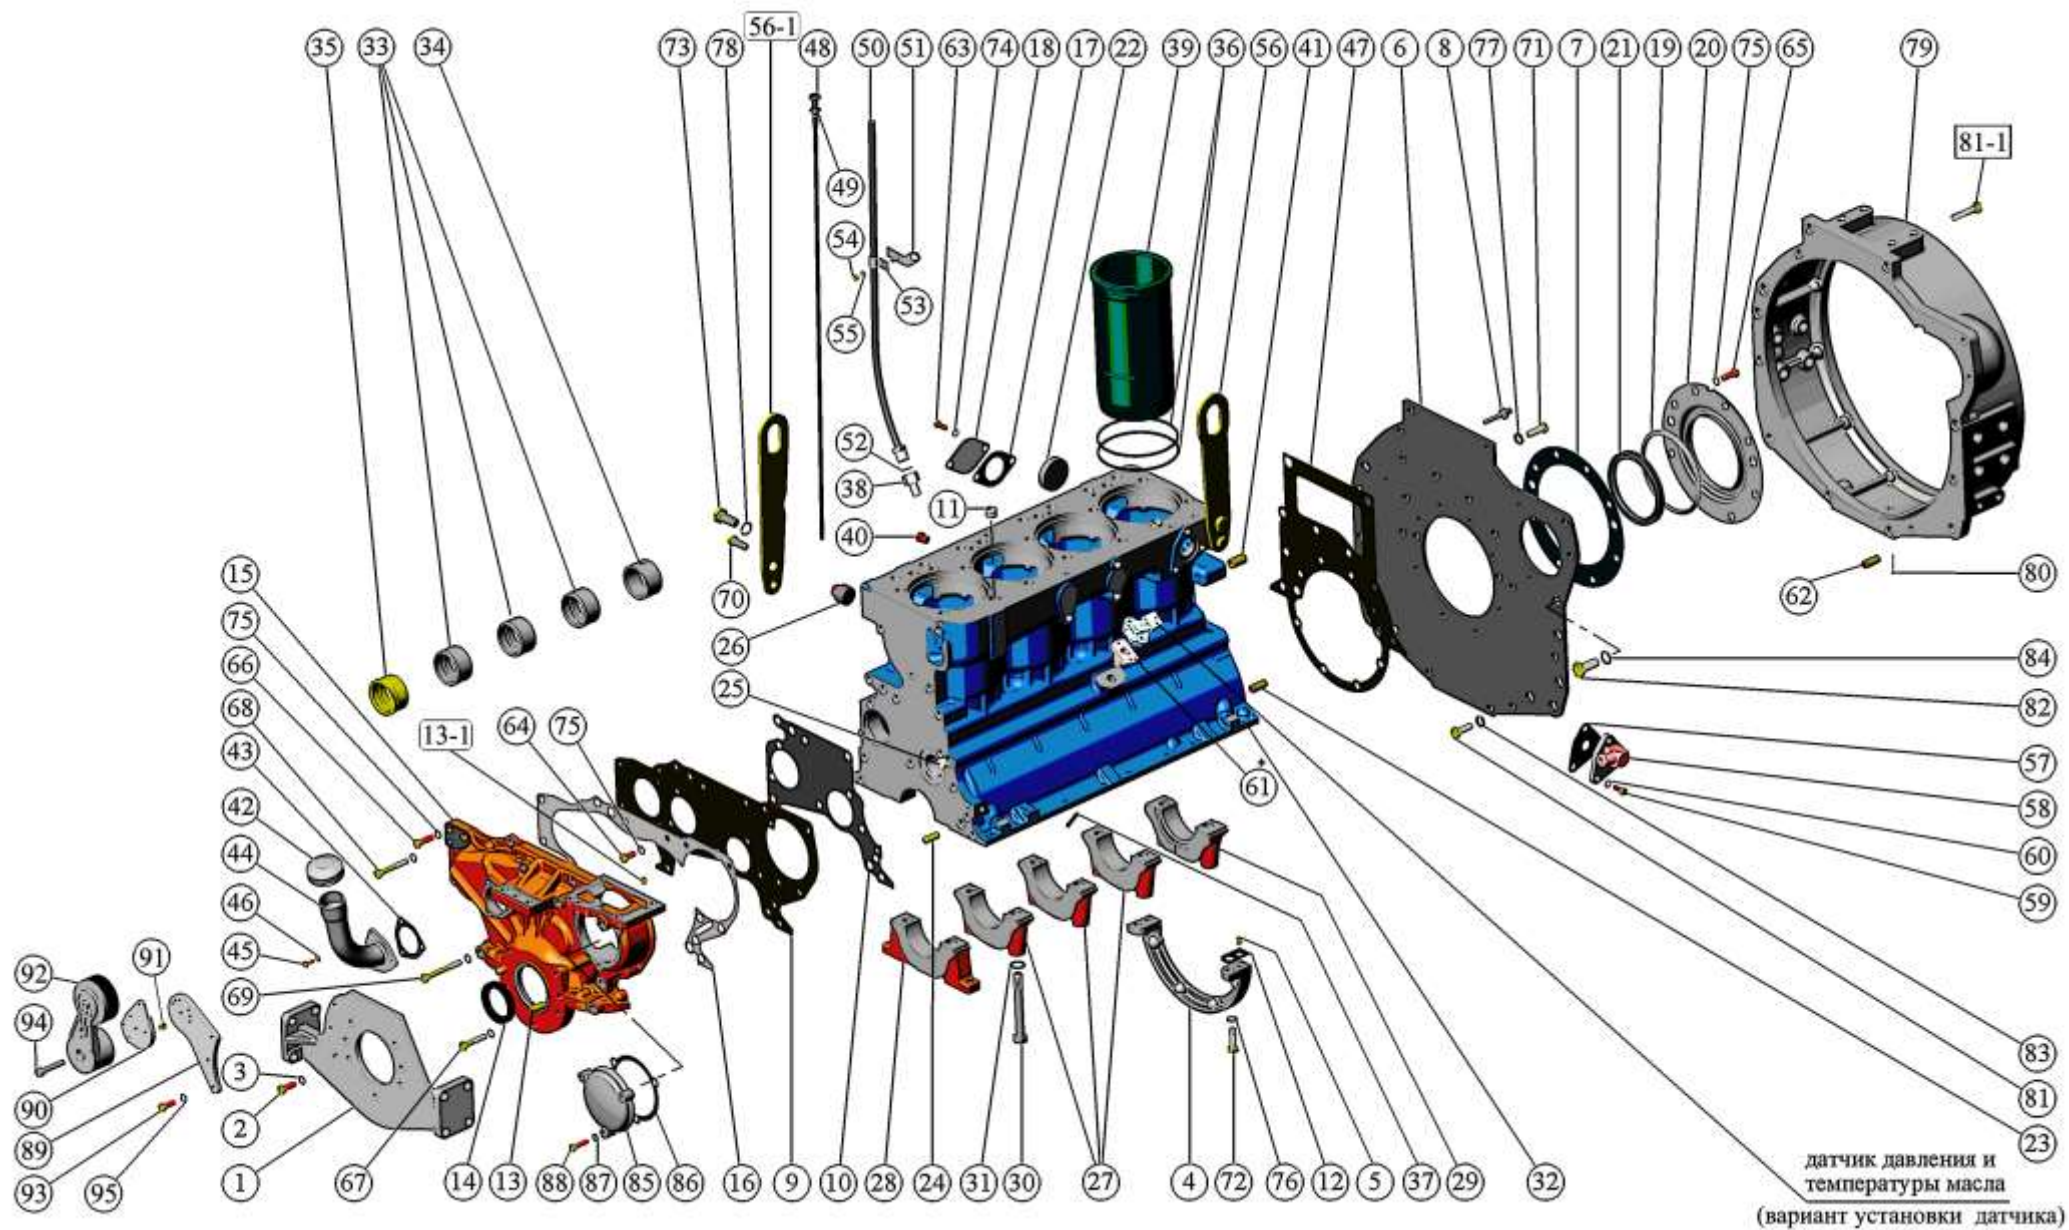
Блок цилиндров. Установка передней опоры. Установка механизма натяжения ремня.
